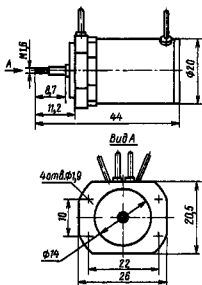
Габаритные и установочные размеры двигателя T16/6M1
